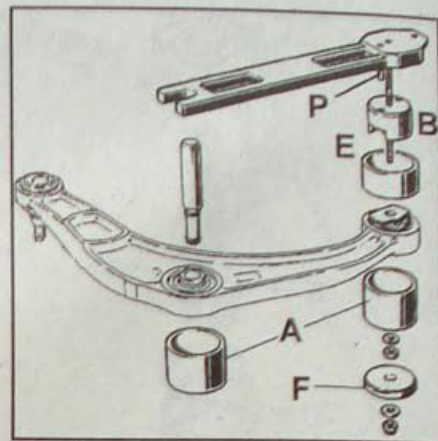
Запрессовка заднего сайлент-блока в нижний рычаг передней подвески:
